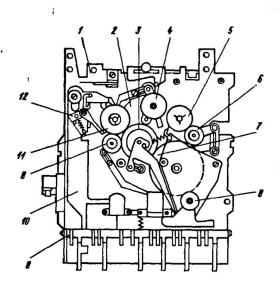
Общий вид ЛПМ (вид сверху):
